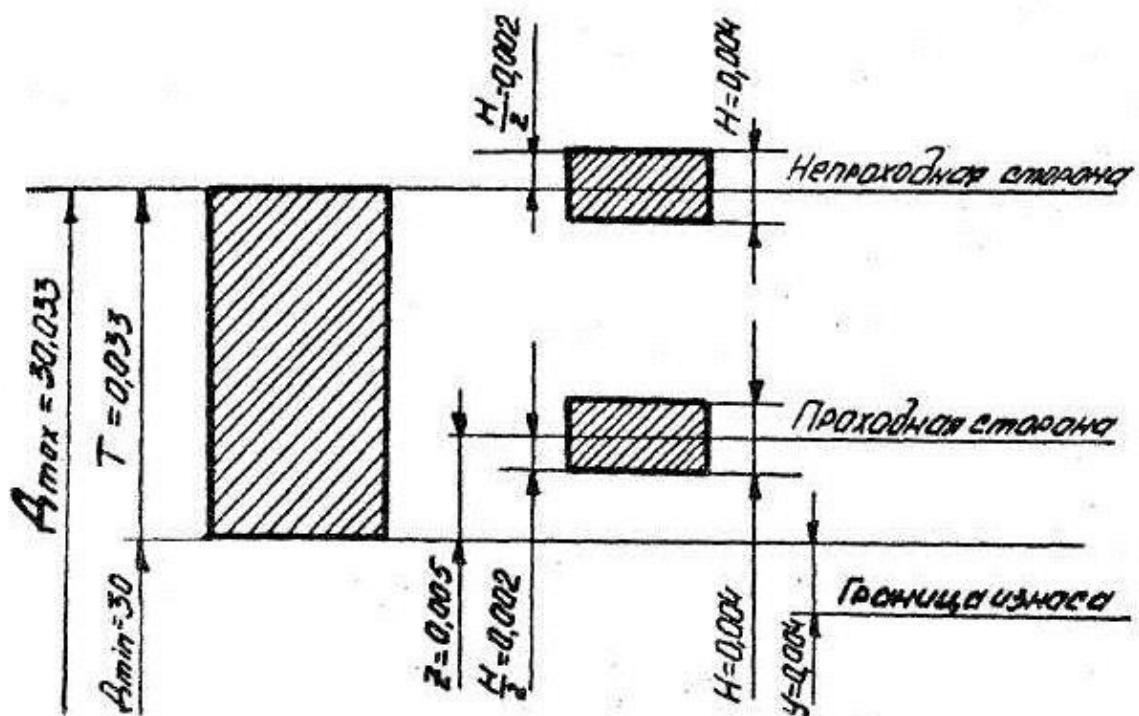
Схема расположения полей допусков калибров
